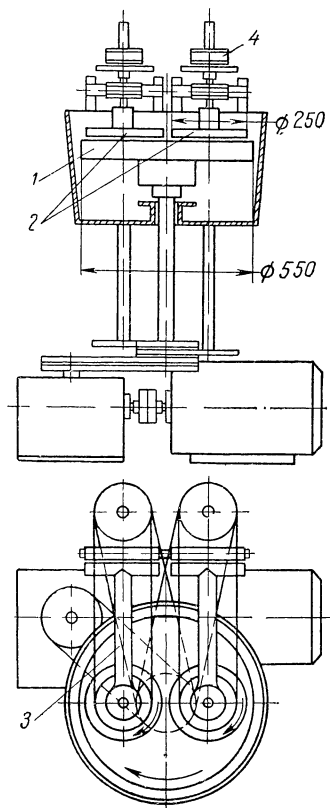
Схема станка для односторонней шлифовки с вращающимся шлифовальником и шайбой.
